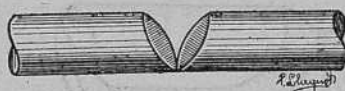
Preparación para la soldadura de barras redondas, hasta 15 mm.
